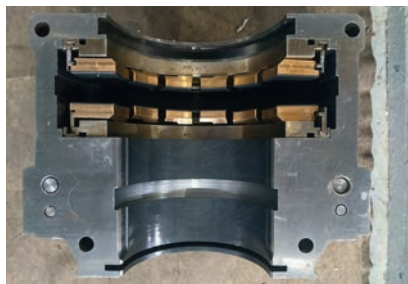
Опорно-упорный подшипник ротора осевого компрессора турбины высокого давления после 6284 ч эксплуатации
